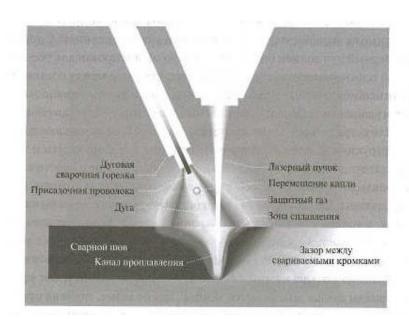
принцип лазерной гибридной сварки
